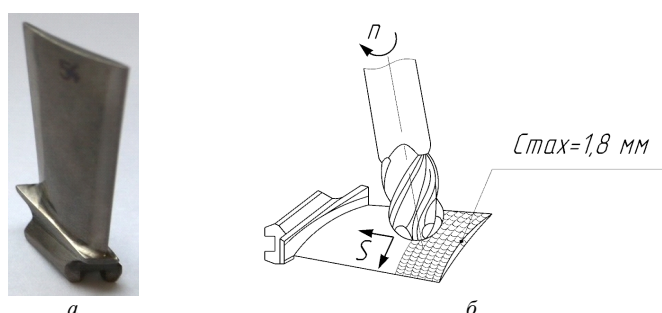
Общий вид лопатки компрессора высокого давления ГТД (а) и схема фрезерования пера (б)
